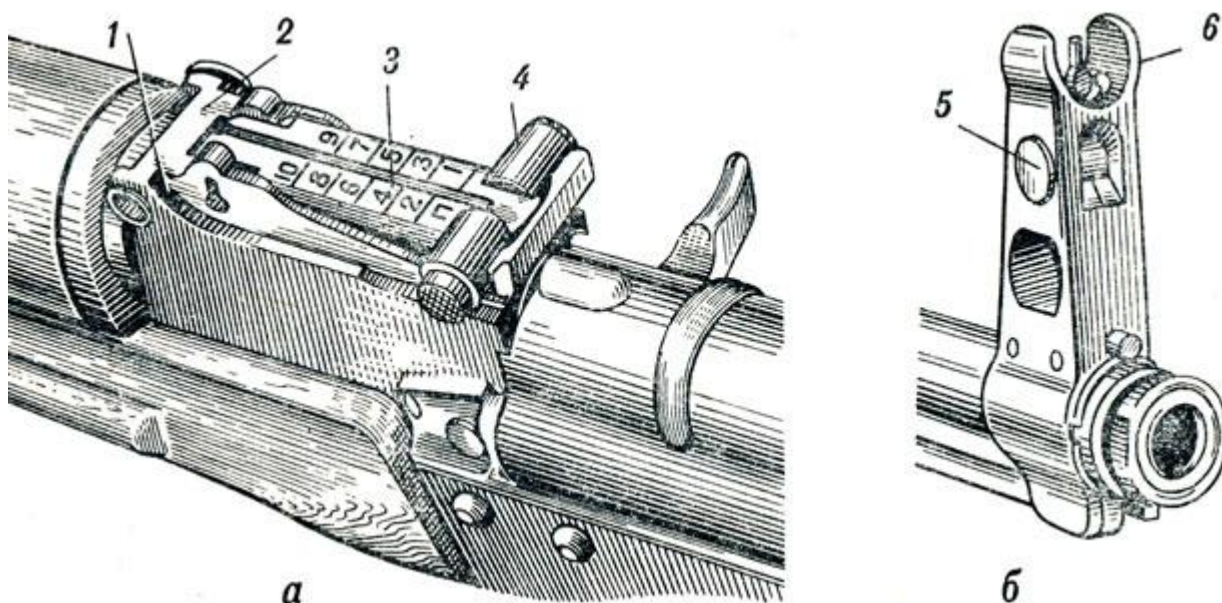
Прицельное приспособление: а - прицел; б - основание мушки; 1 - колодка прицела; 2 - пластинчатая пружина; 3 - прицельная планка; 4 - хомут; 5 - полозок с мушкой; 6 - предохранитель мушки
